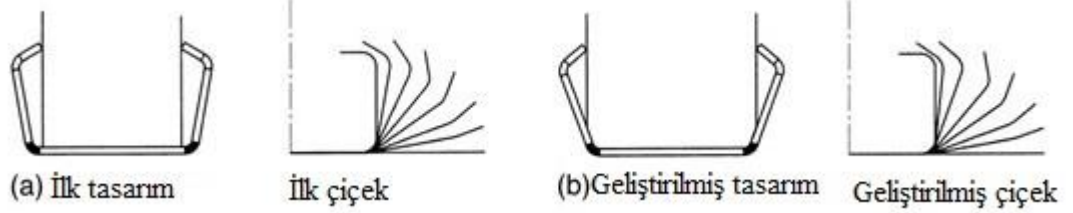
Makara ile şekillendirilmiş sac malzemenin çiçek diyagramı [4].
